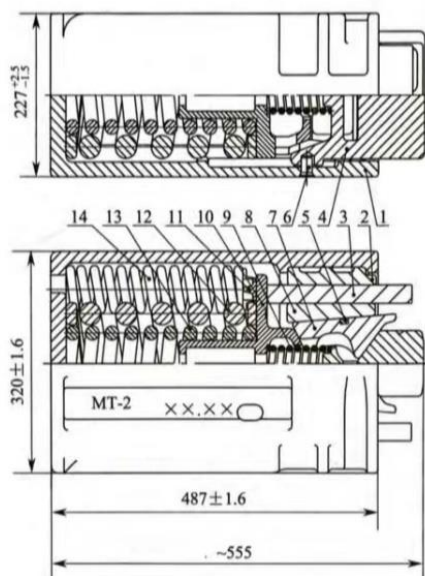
Буфер типа МТ-2: 1-коробка; 2-наружная фиксирующая пластина; 3-подвижная пластина; 4-центральный клин; 5-медный пруток; 6-укораченный штифт; 7-клин; 8-неподвижная наклонная плита; 9-пружина восстановления; 10-пружинное седло; 11-угловое пружинное седло; 12-наружная цилиндрическая пружина; 13-внутренняя циркулярная пружина; 14-угловая пружина.
